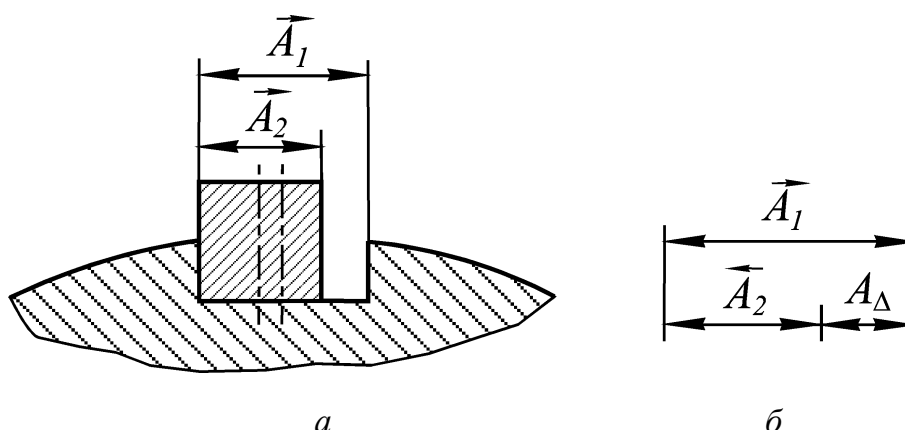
Сопряжение шпонки с валом (*а*) и сборочная размерная цепь для данного сопряжения (*б*)
